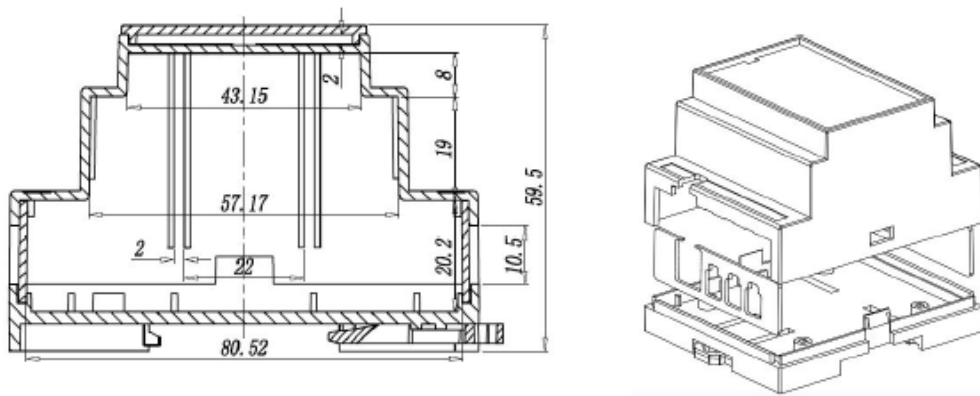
Vista frontal dimensiones Wenu Trifásico
